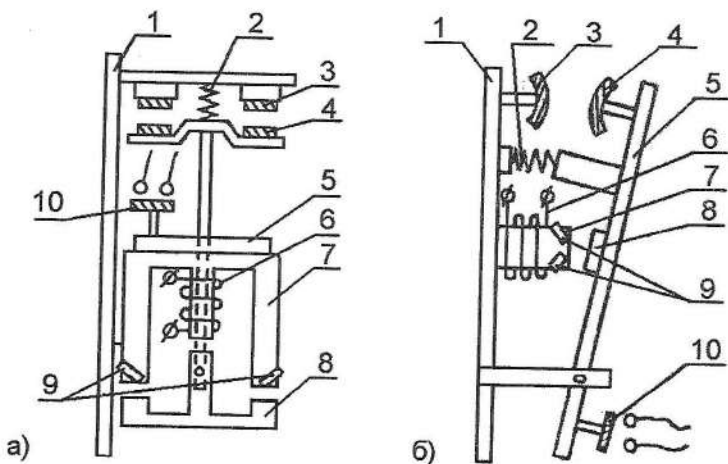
Устройство магнитных пускателей с прямоходовой Ш-образной (а) и поворотнорычажной П-образной (б) магнитными схемами: 1 – основание; 2 – пружина; 3 – неподвижный контакт; 4 – подвижный контакт; 5 – траверса; 6 – катушка; 7 – сердечник; 8 – якорь; 9 – короткозамкнутый виток; 10 – мостик блок-контактов.
